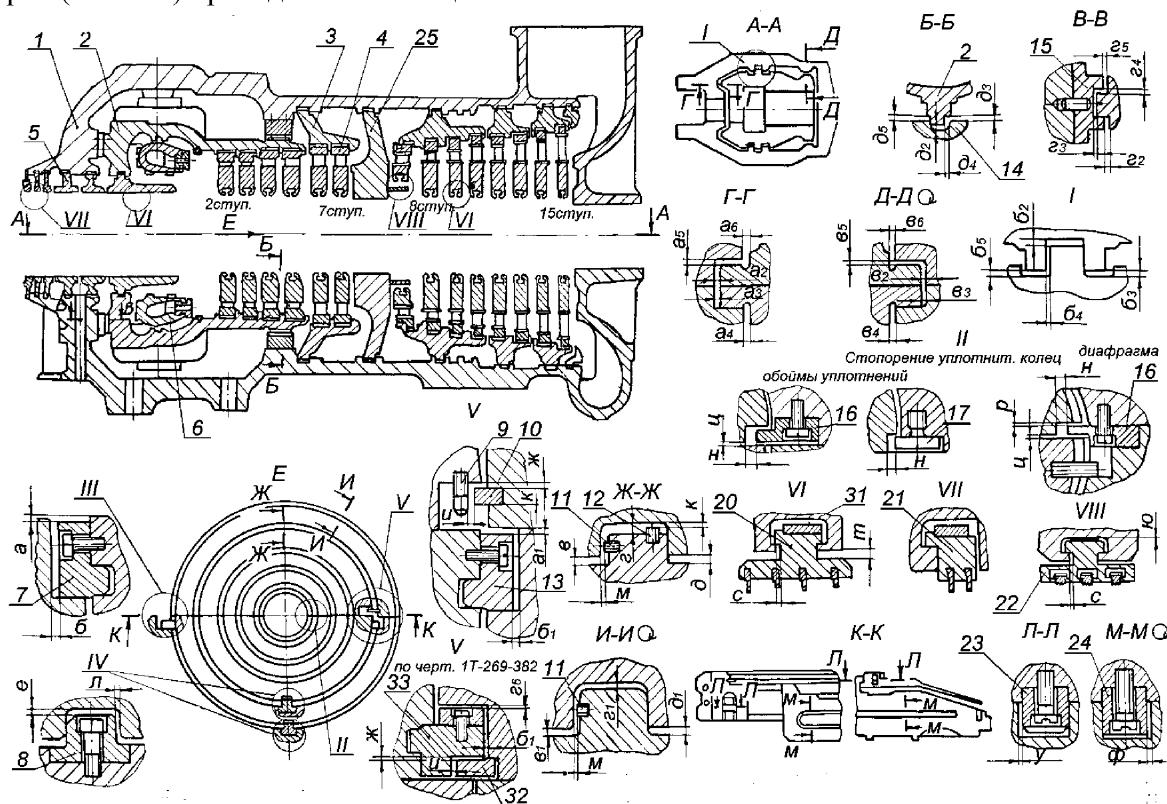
, лист 1 – Корпусные части цилиндра ВД
